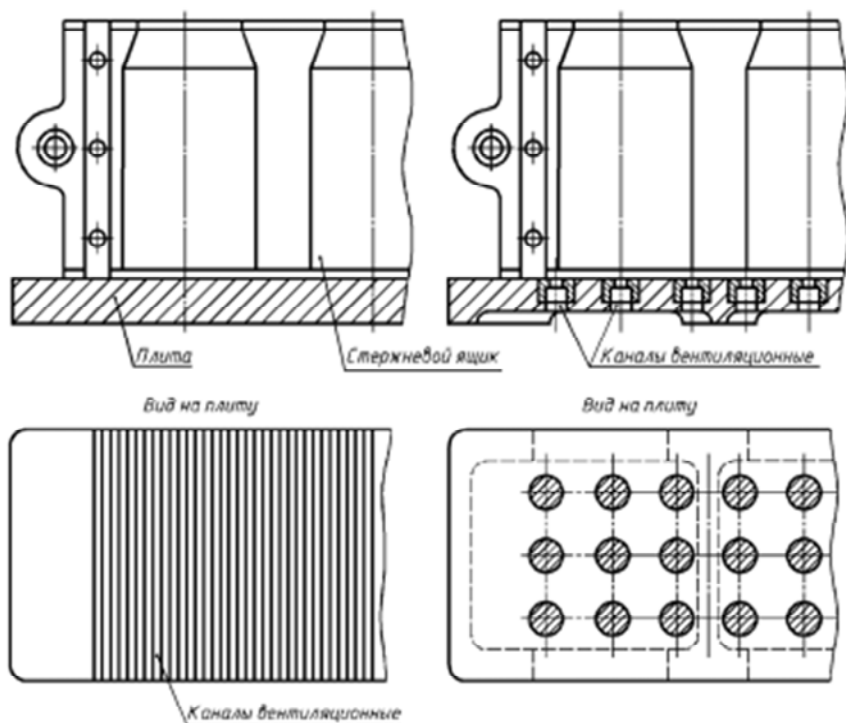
Примеры установки стержневого ящика на вентиляционную плиту
